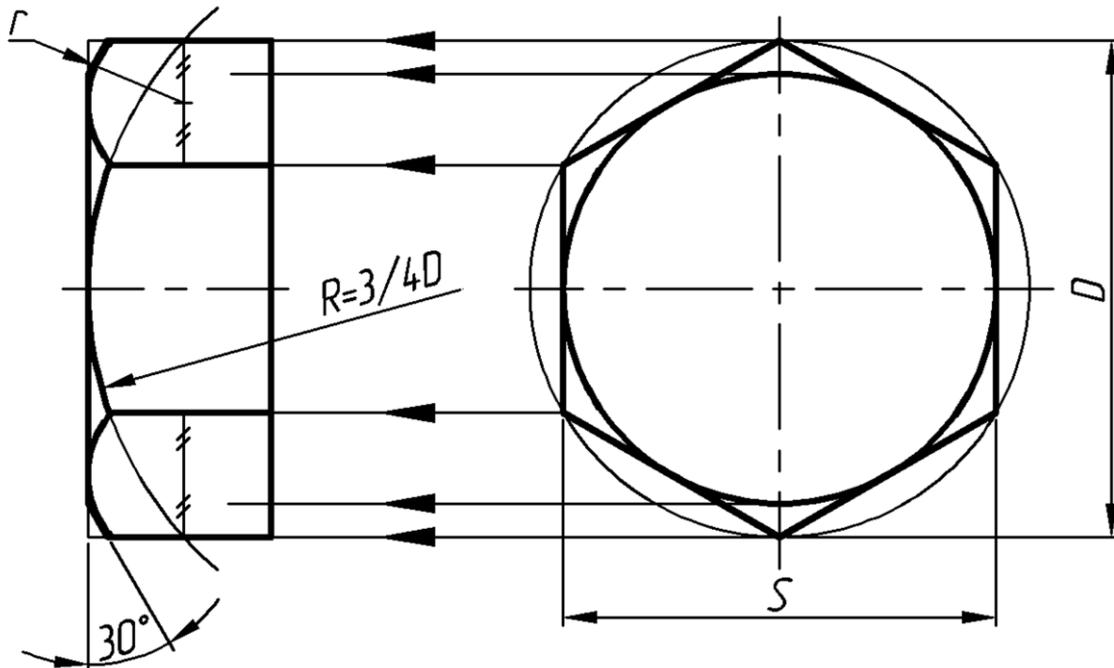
Шестигранная головка болта и гайка с конической фаской
